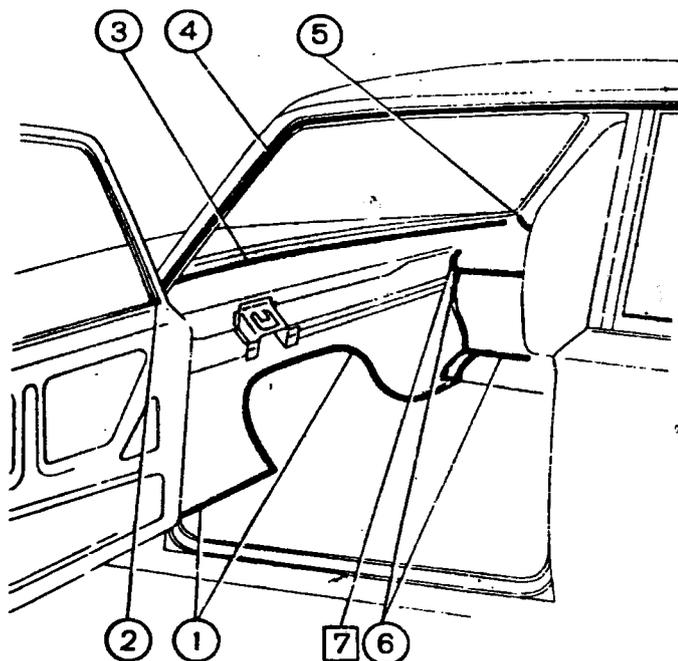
Сварные швы и стыки, на которые наносится уплотнительная мастика (вид кузова с внутренней стороны): 1 - щитка передка с ковром пола и с полом; 2 - рамок передних и задних дверей; 3 - внутренней панели рамы ветрового окна с верхней панелью передка; 4 - сточного желобка крыши с боковиной (снизу); 5 - основания передней стойки; 6 - боковины с щитком передка и полом; 7 - боковой панели передка с верхним усилителем передка
